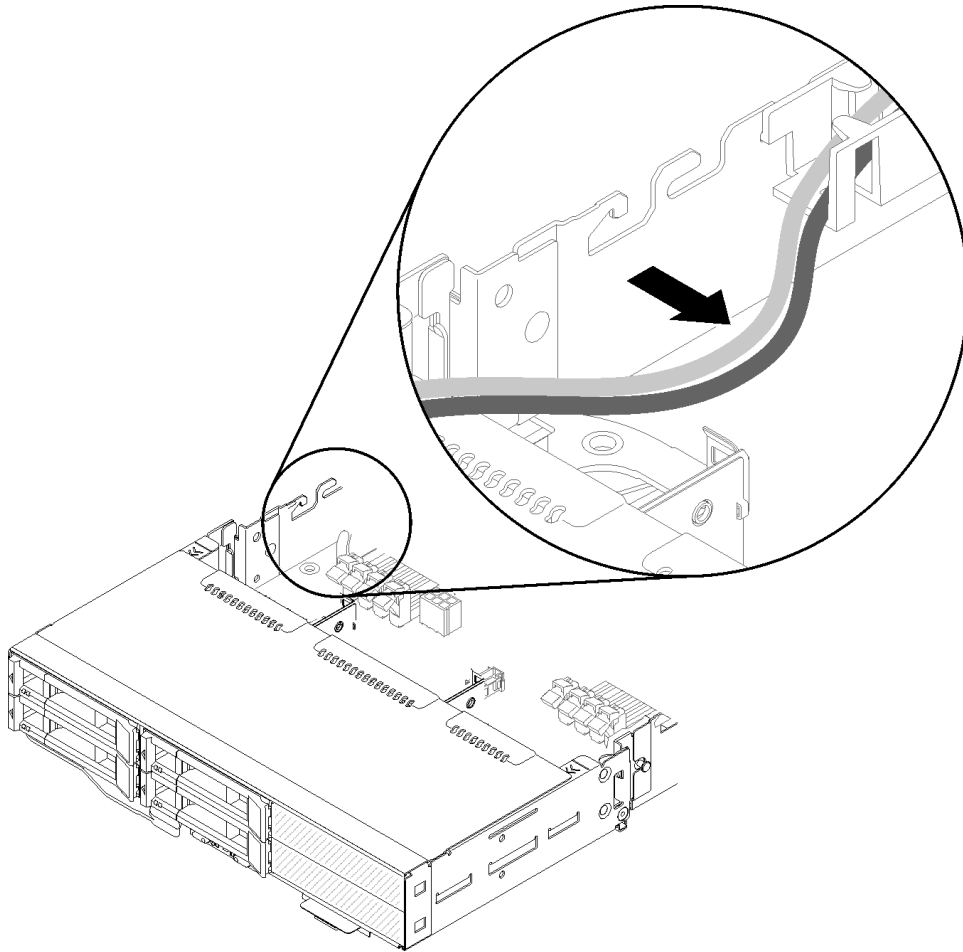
Retirada de cables para dar espacio al elemento de sujeción de cables
